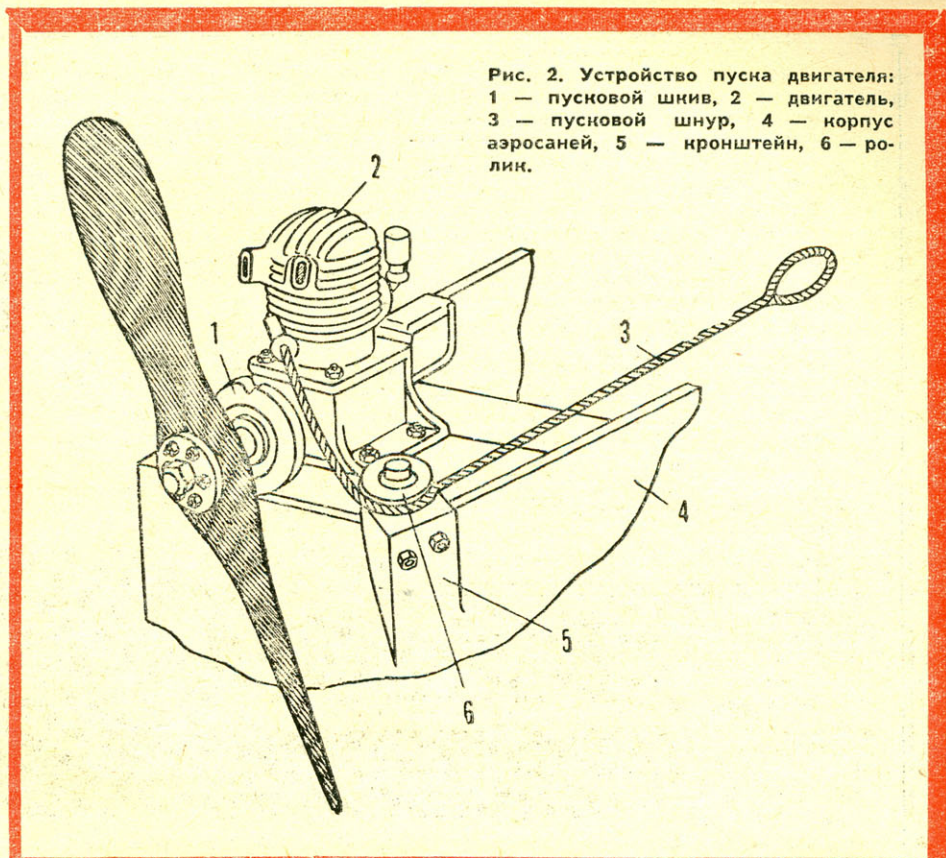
Устройство пуска двигателя: 1 — пусковой шнив, 2 — двигатель, 3 — пусковой шнур, 4 — корпус аэросаней, 5 — кронштейн, 6 — ролик.
